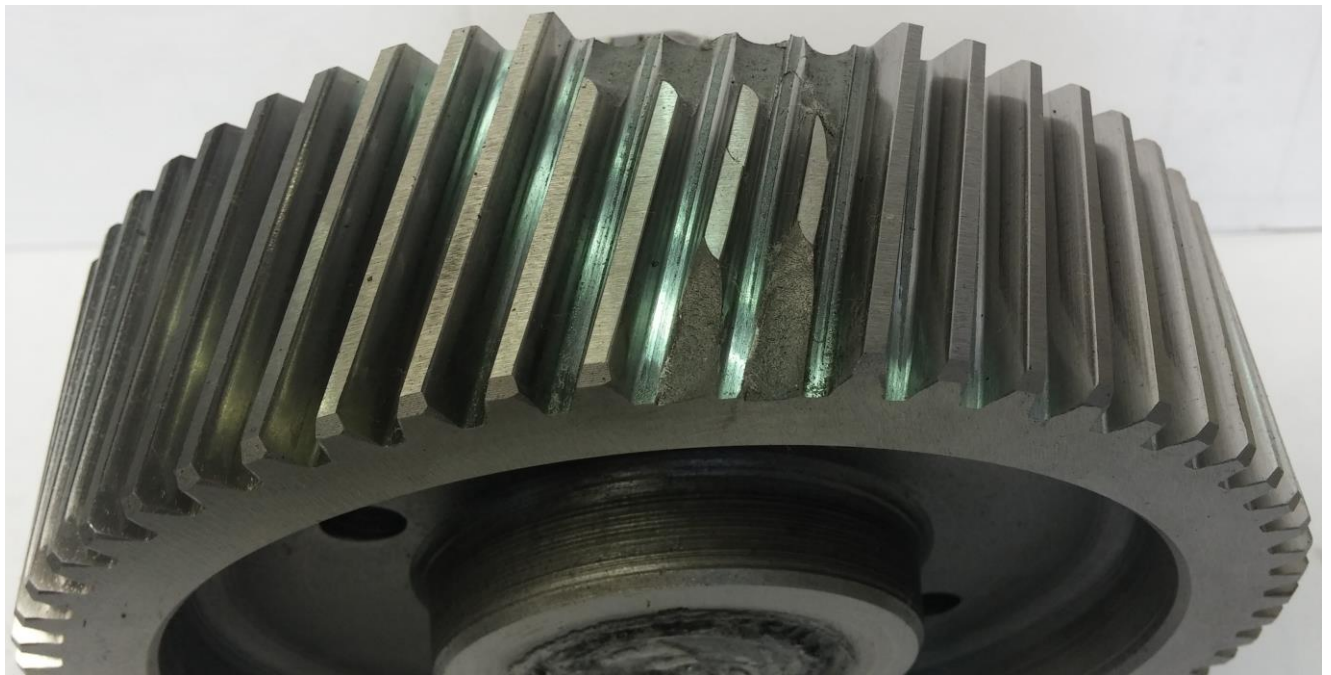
Внешний вид колеса первой ступени редуктора с эвольвентным зубчатым зацеплением после испытаний
